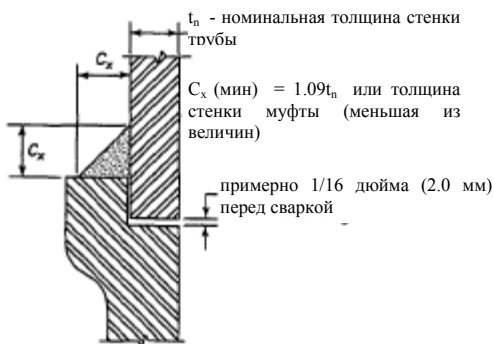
(С). Минимальные сварочные размеры, требуемые для муфтовой сварки компонентов, отличных от фланцев.
